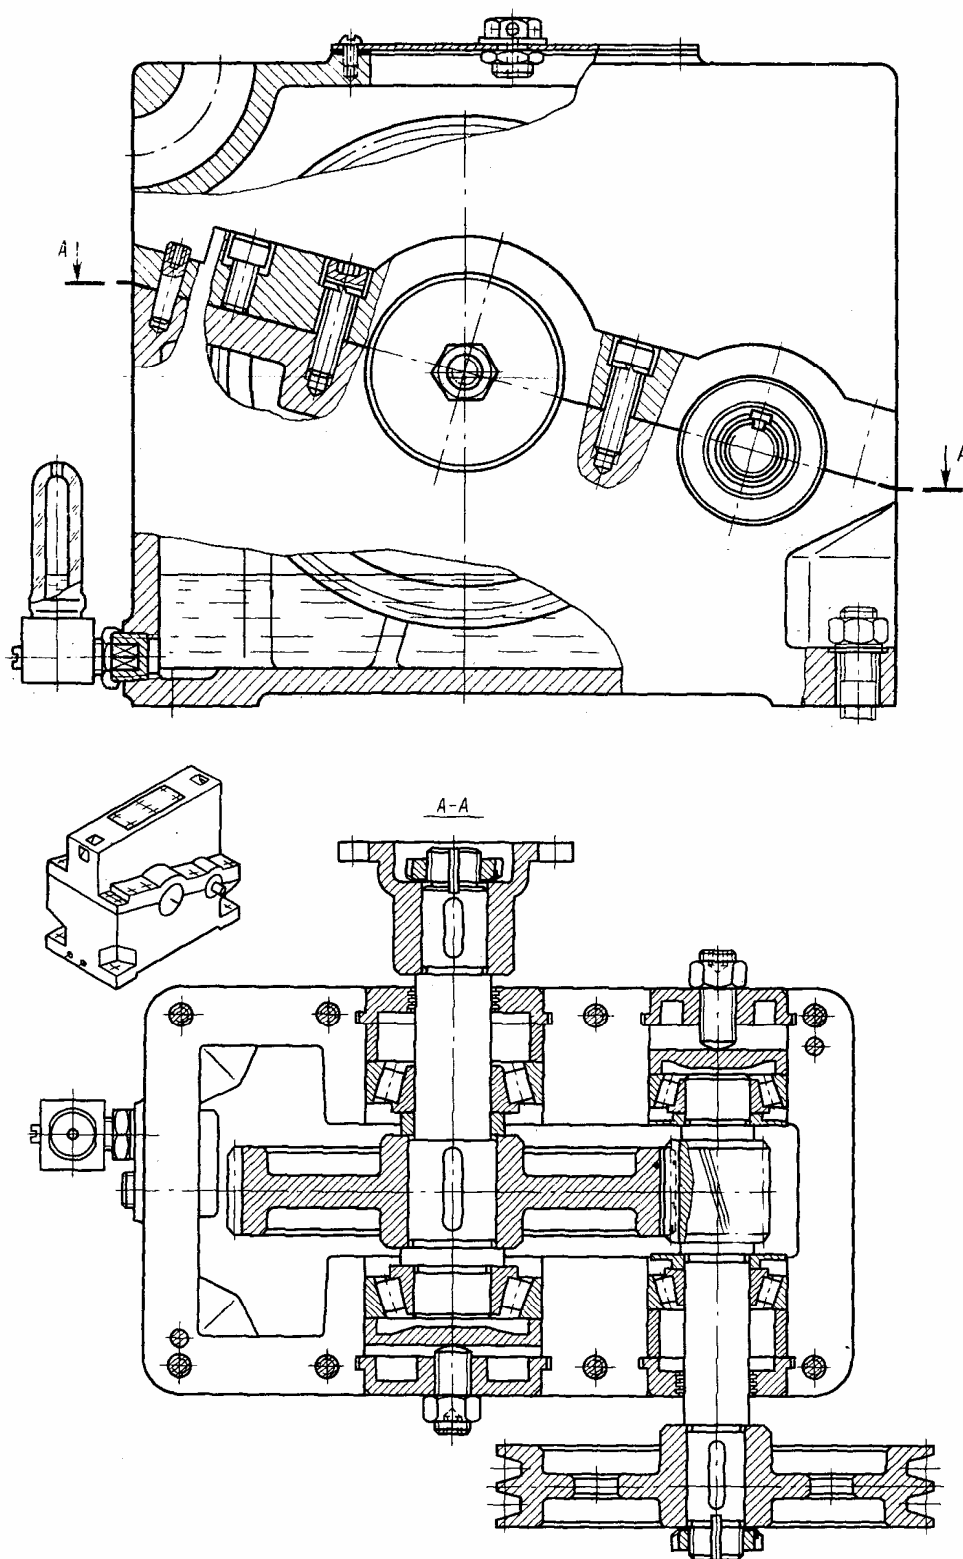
Редуктор (А5) цилиндрический одноступенчатый горизонтальный с наклонным разъемом корпуса
